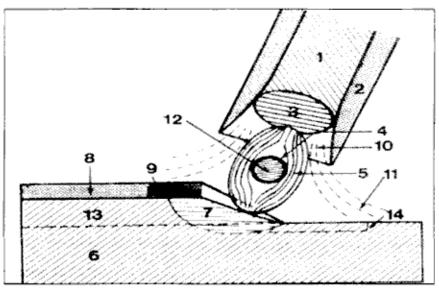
Fusión de Electrodo Fuente: Manual de Soldadura OERLIKON [44]
